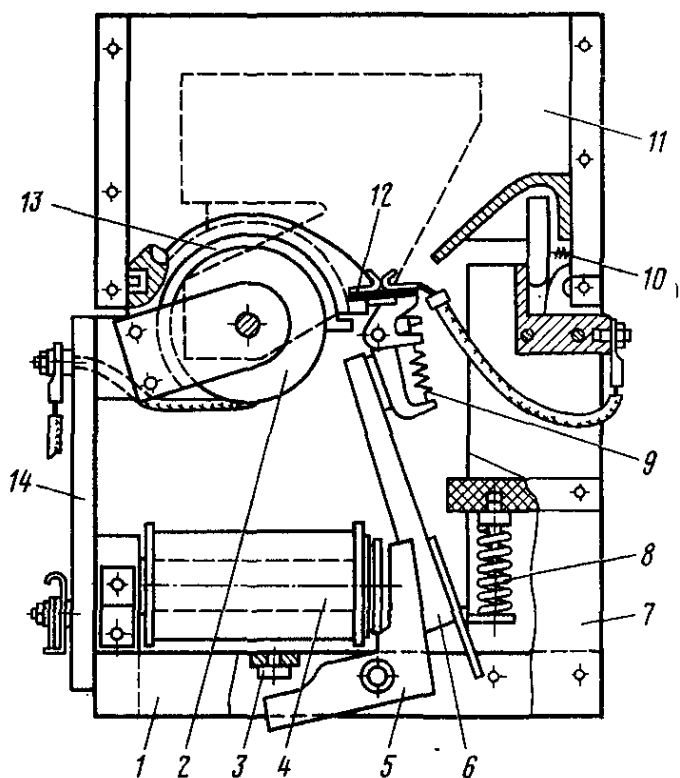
Электромагнитный контактор МК-310Б-34 (33, 38):
